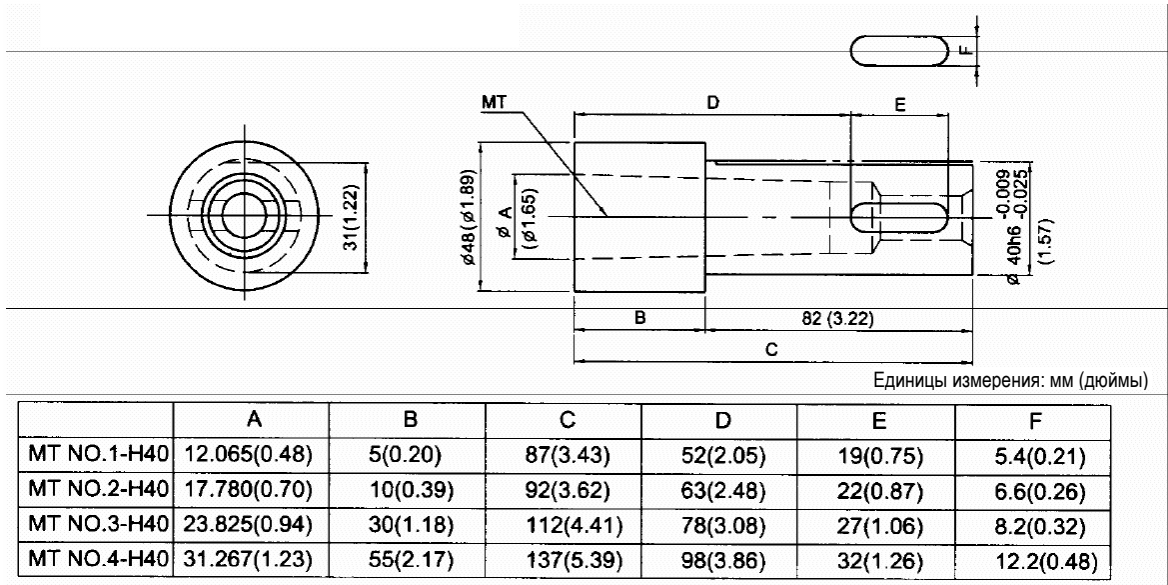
Габариты резцедержателя (втулка сверла)
